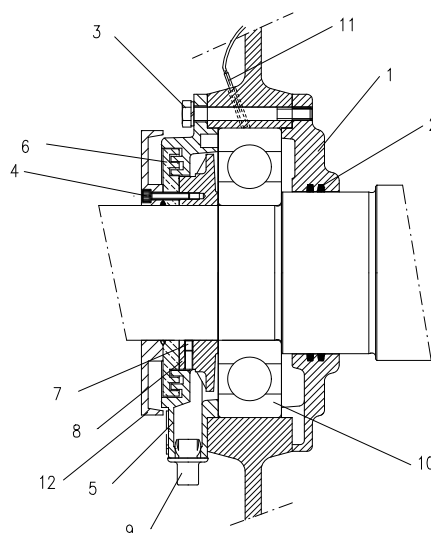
Детали смазываемого консистентной смазкой подшипника качения
